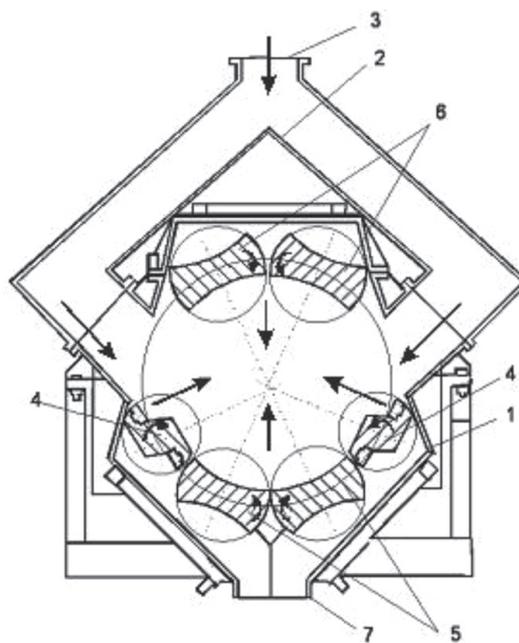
Кинематическая схема дробилки ДКД-300: 1 – корпус дробилки; 2 – делитель исходного материала; 3 – питающий патрубок; 4 – роторы первичного дробления; 5 – роторы дополнительного дробления; 6 – роторы вторичного дробления; 7 – разгрузочный патрубок
